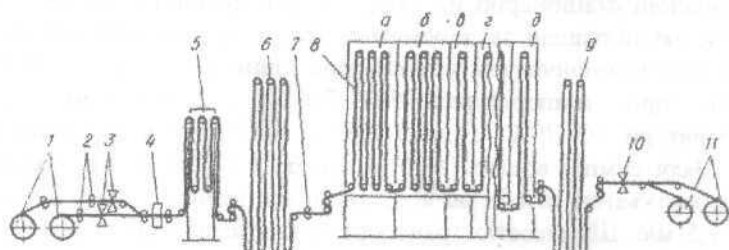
Схема безперервного агрегату відпалу штаби: 1-розмотувач; 2-тягнучі ролики; 3-ножиці; 4-зварювальний агрегат; 5-ванни електролітичного очищення штаби; 6; 9-петльонакоплювачі; 7-дисккові ножиці; 8-під для відпалу (камери: а-витримки, б-сповільненого охолодження; в-прискороеного охолодження, г-остаточного охолодження); 10-ножиці; 11-моталка.
